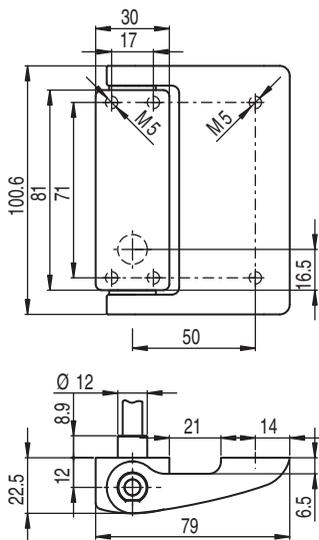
Dimensões do S410-M4-CB02M12-W e do S410-M4-CB2PUR-W em mm
